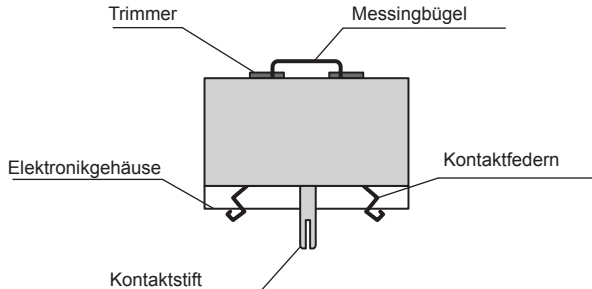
Seitenansicht des Elektronikmoduls des Füllstandsmessers
